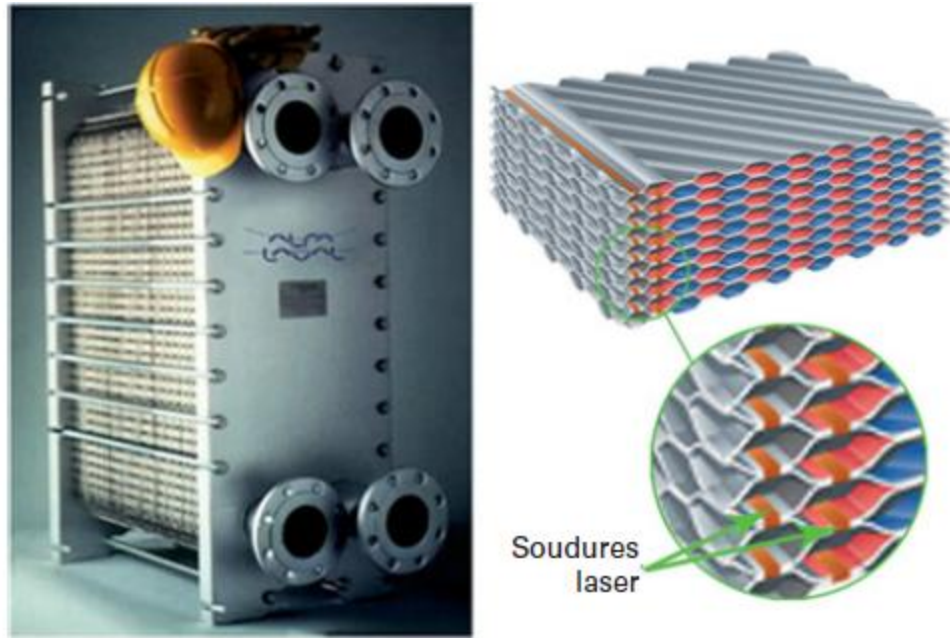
Échangeur à plaques tout soudé [5].
